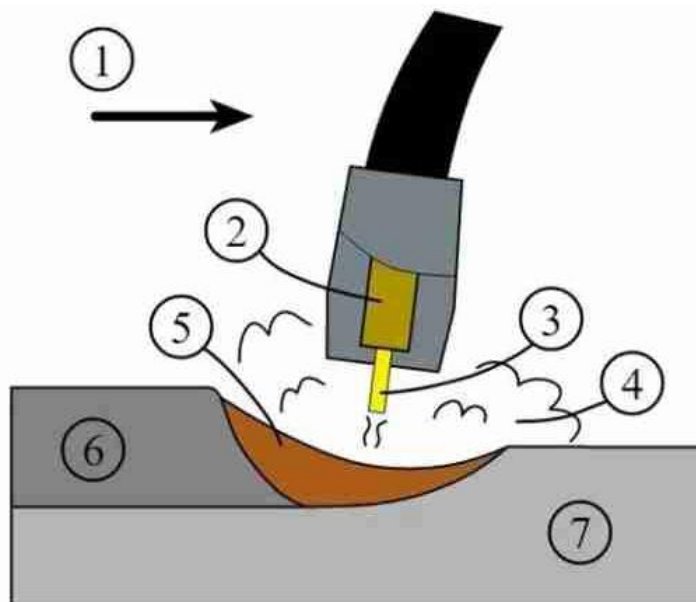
Схема выполнения ручной дуговой сварки
